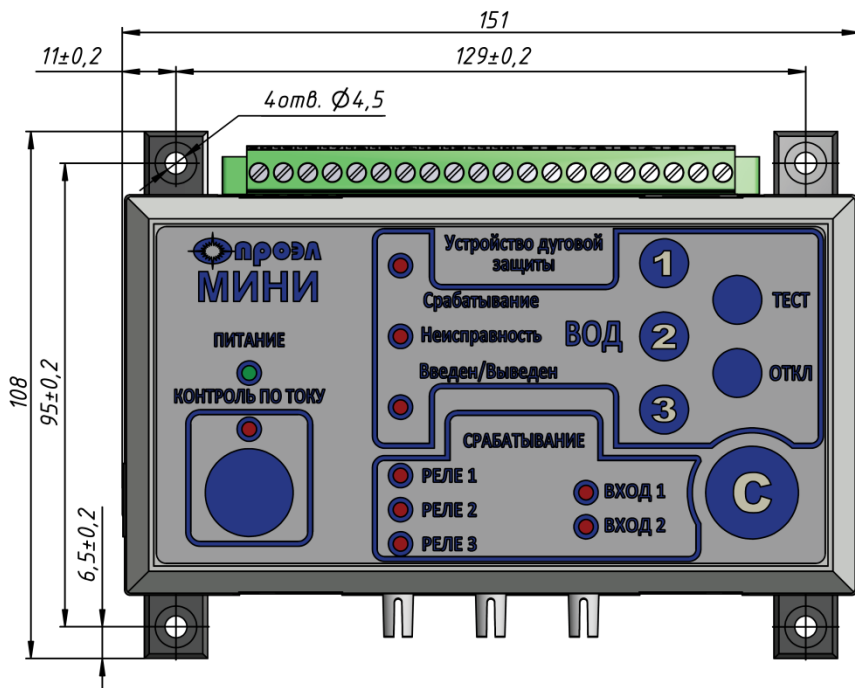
Вид и габаритные размеры БПМ в варианте крепления 00
